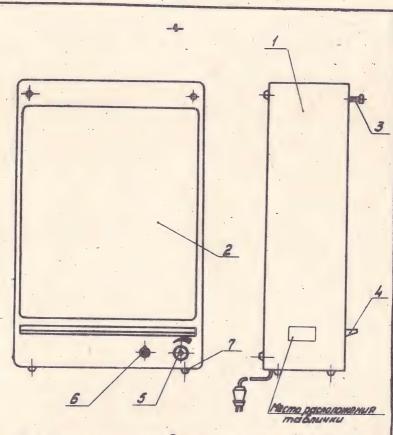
Негатоской общего назначения Н-48. 1-корпус; 2-экран; 3-кранштейн; 4-желоб; 5-регулятор яркости; 6-выключатель; 7-ножка.
